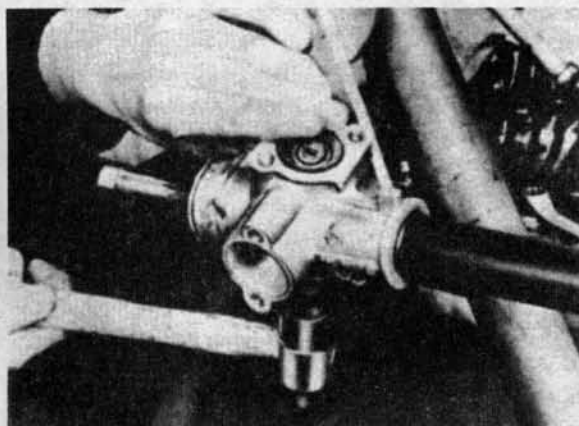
Снятие подшипников зубчатого вала в старом варианте механизма
